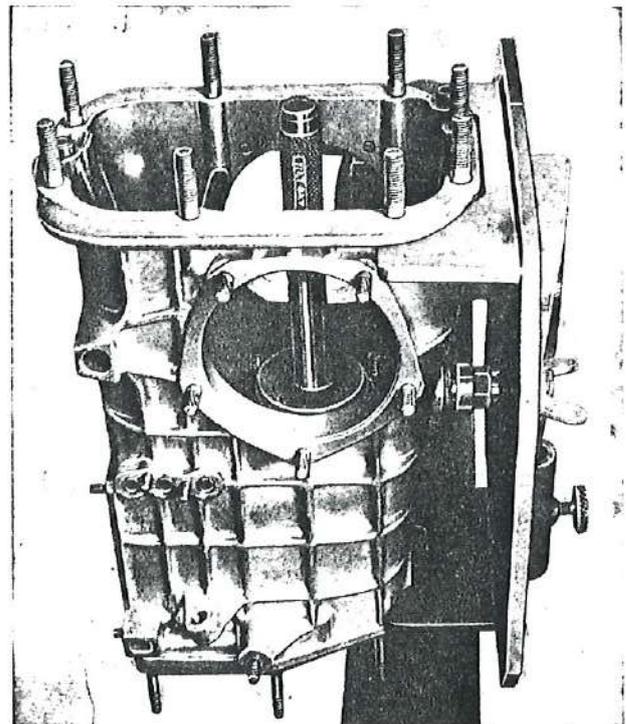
Montaje del rodamiento a bolas posterior del piñón cónico con el útil A. 62001.
